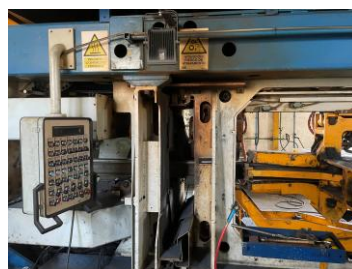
Máquina de soldadura de carril de 60kg/m. Fuente: Propia
